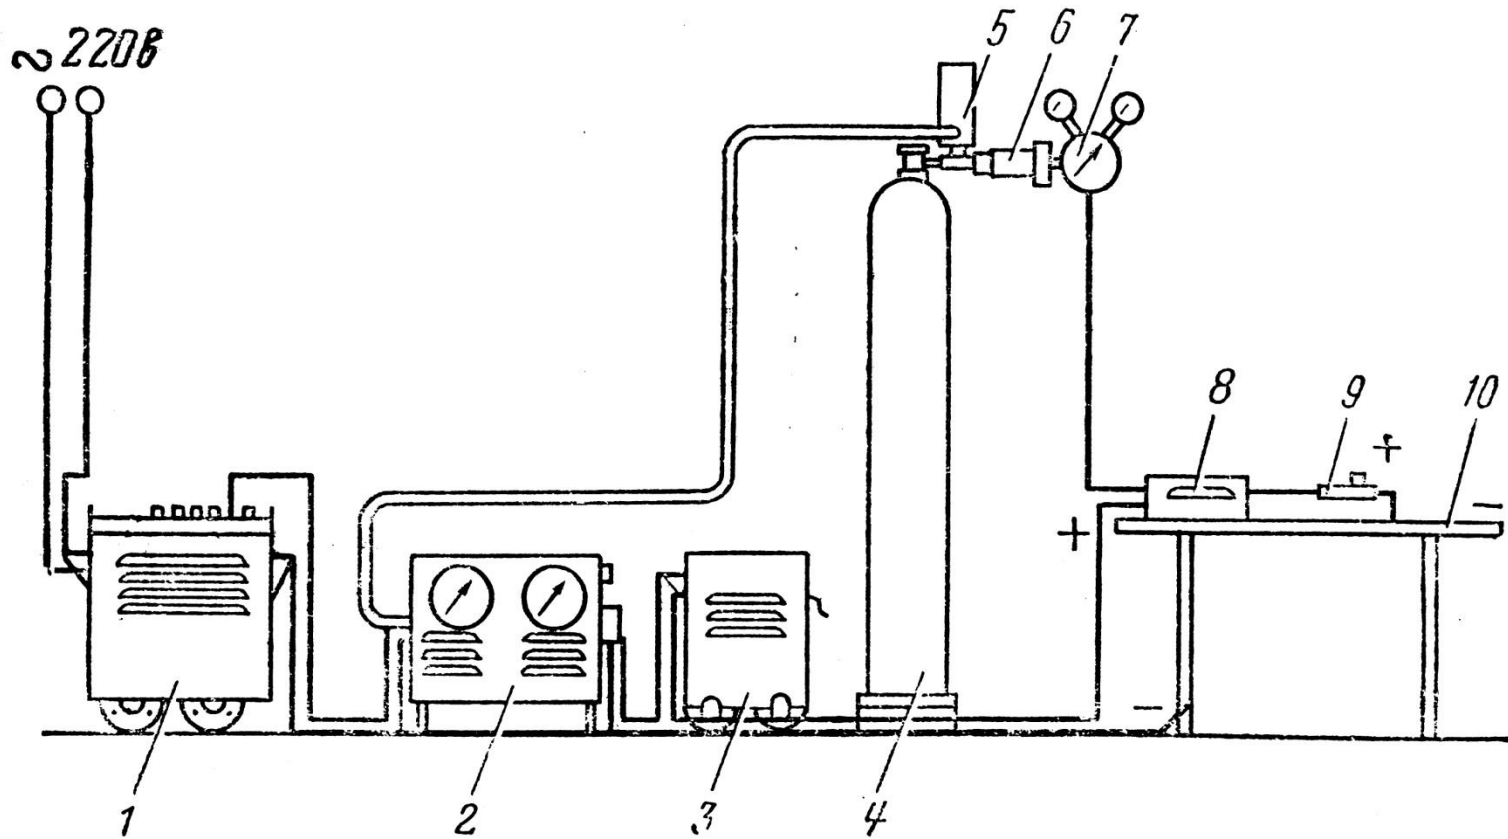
Схема установки для полуавтоматической сварки деталей в защитной среде углекислого газа:
